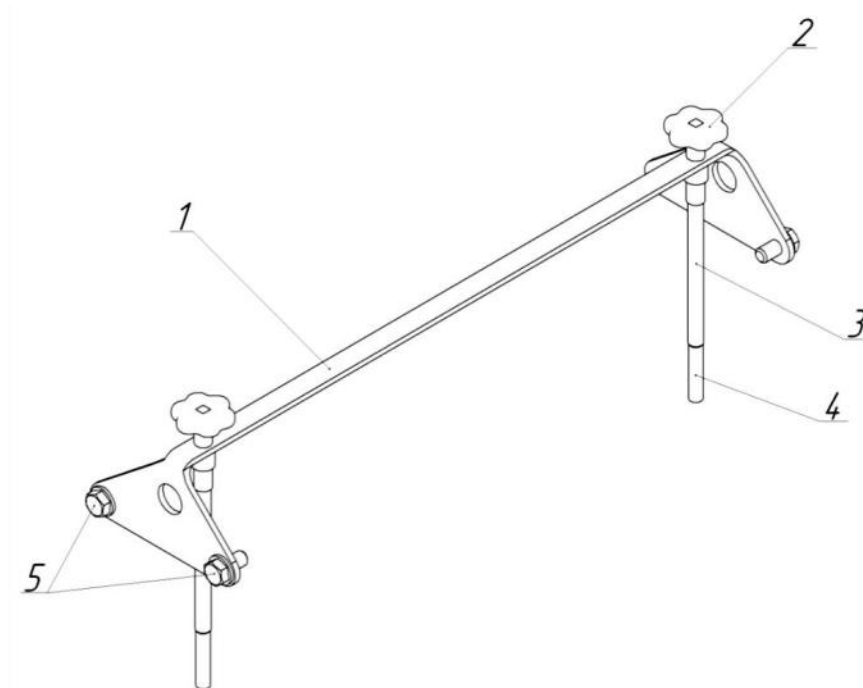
Пристрій для зняття головки блока циліндрів двигуна автомобіля:
